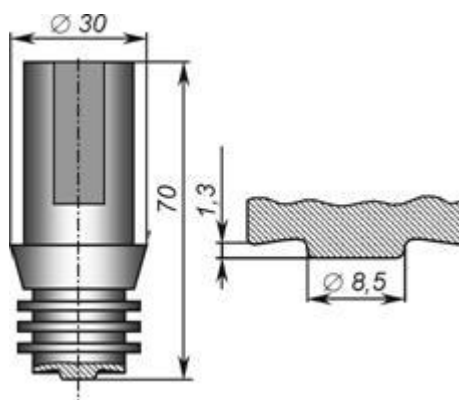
Конструкция инструмента, применяемого для сварки листов толщиной 8 мм из алюминий-литиевого сплава.
